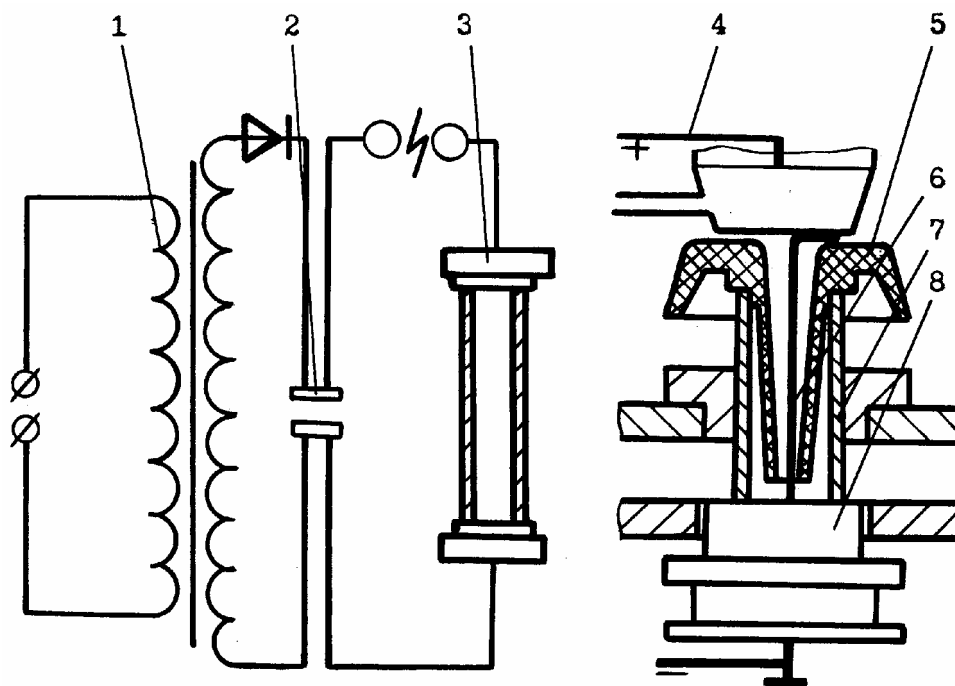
Устройство для электрогидравлической раздачи поршневых пальцев: 1 – источник энергии; 2 – накопитель энергии; 3 – технологический узел; 4 – положительный электрод; 5 – пластмассовый патрон; 6 – проводник; 7 – восстанавливаемая деталь; 8 – отрицательный электрод
